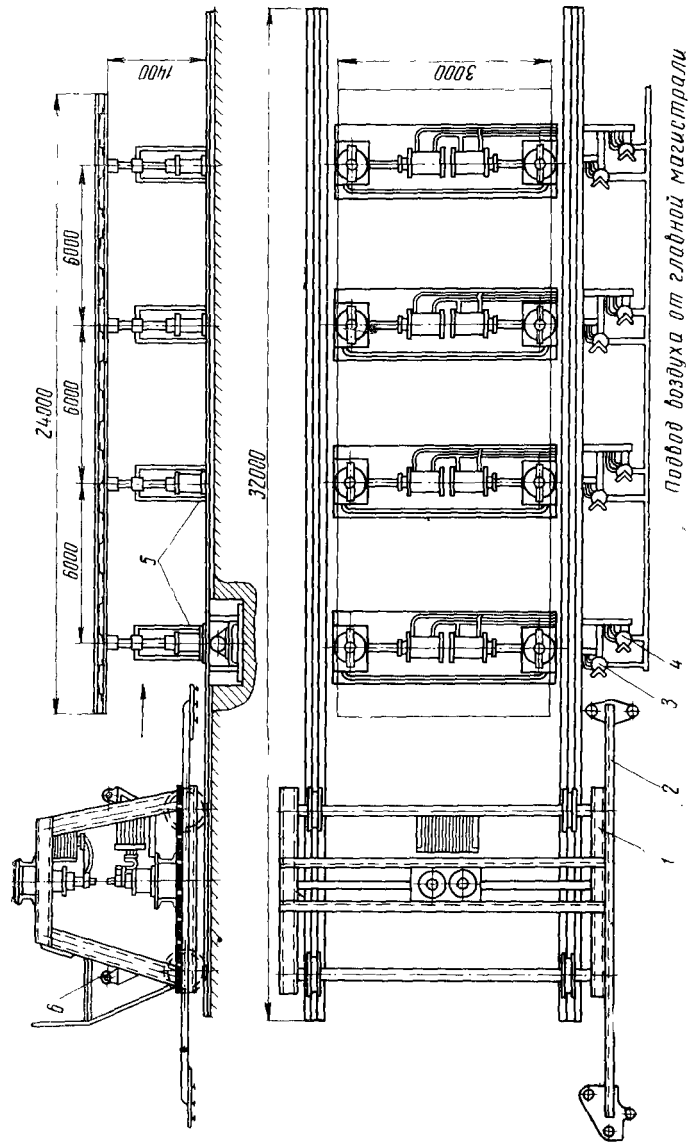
Установка для сварки настила пола вагона
